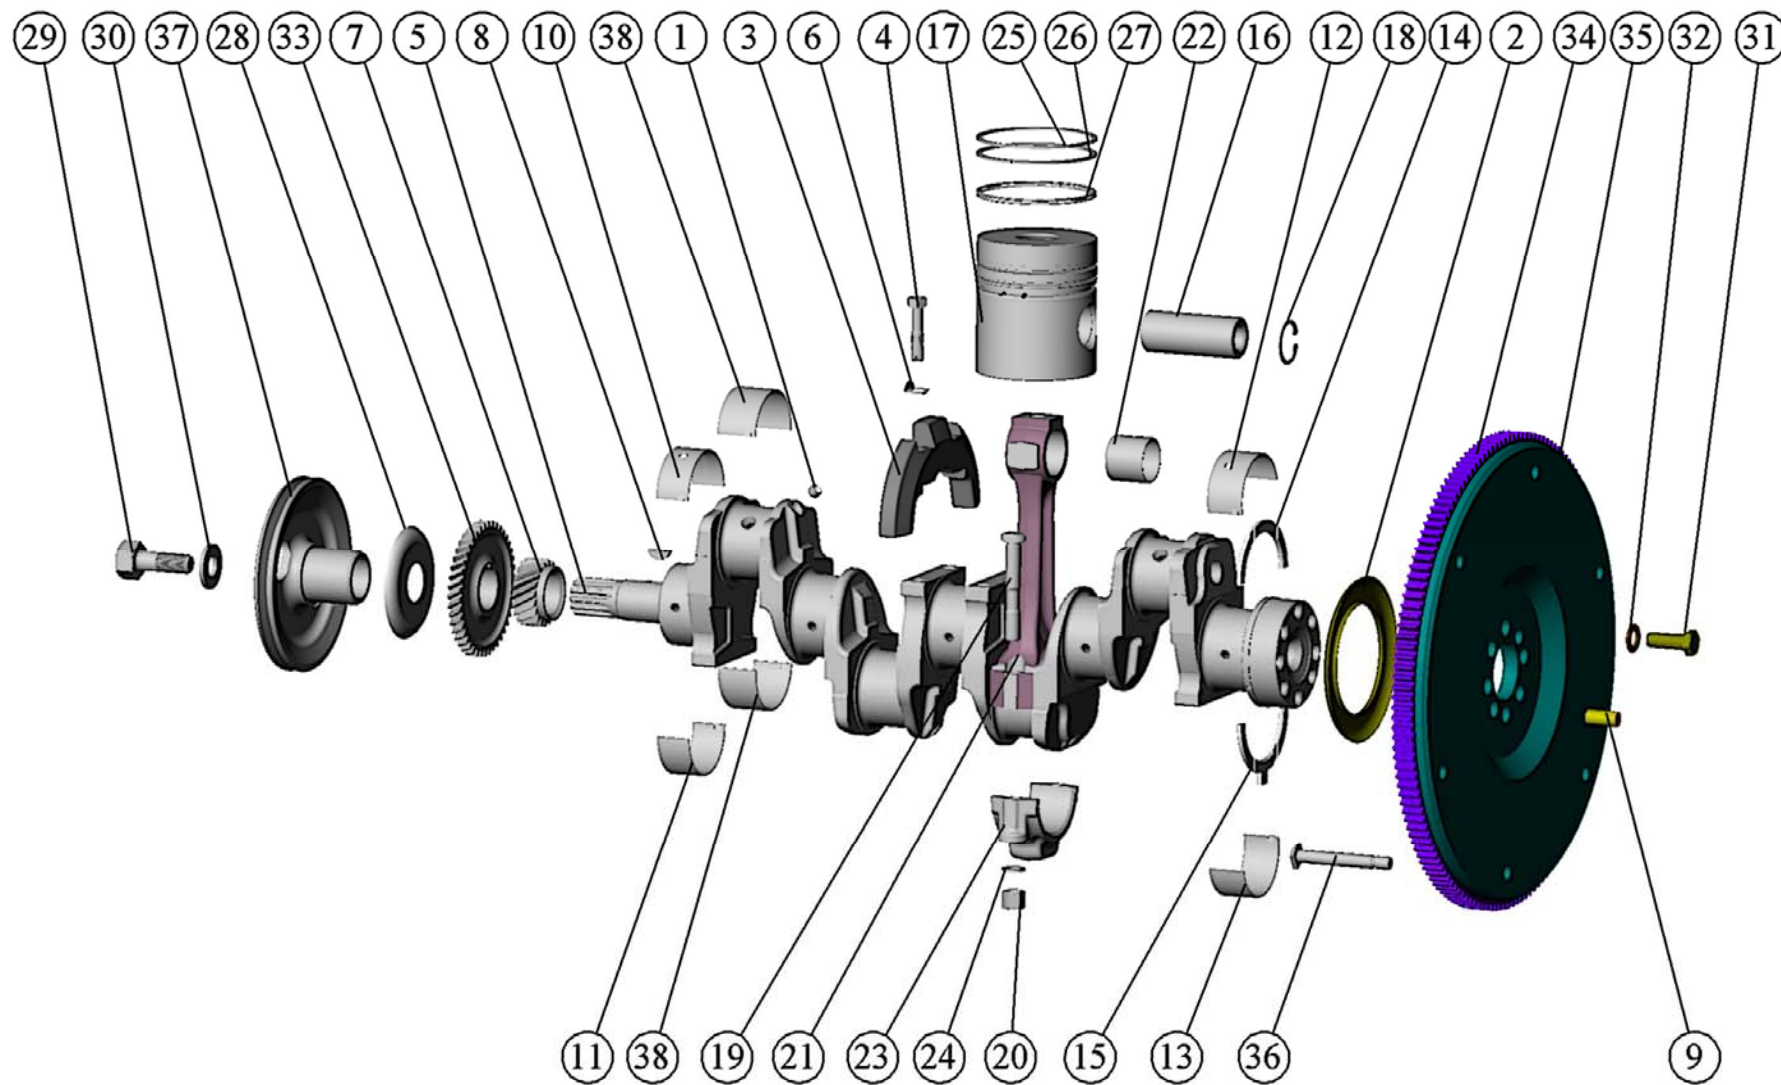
Поршни и шатуны. Коленчатый вал. Маховик
